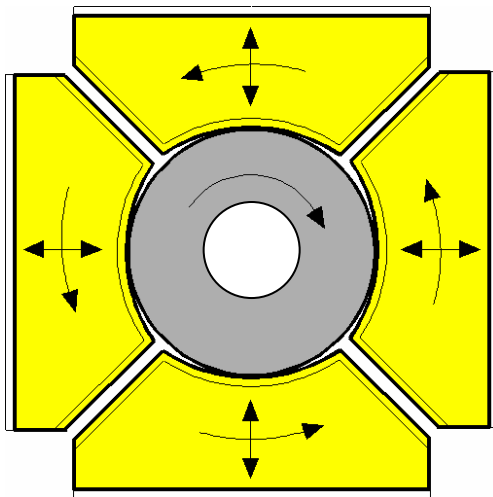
Anordnung der Werkzeuge um ein Werkstück
